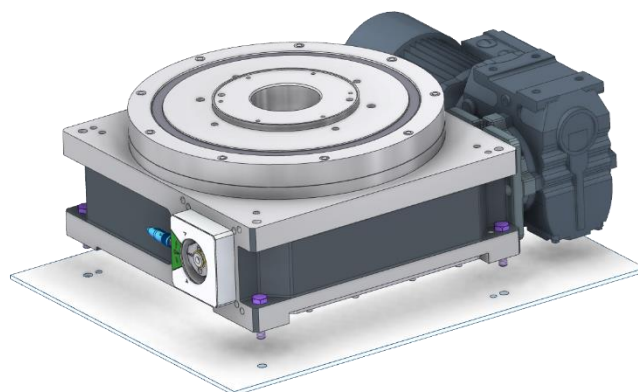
Einbau Trommelkurvenrundtisch - Standardeinbaulage
